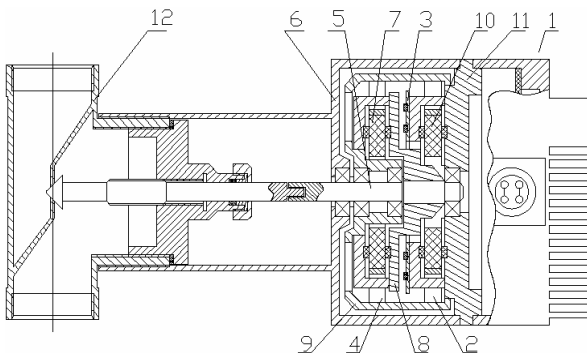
Исполнительный механизм: 1 - защитная крышка блока питания; 2 - толкатели нижнего осциллятора; 3 - токосъемное устройство; 4 - толкатели верхнего осциллятора; 5 - вал; 6 - корпус; 7 - верхний осциллятор; 8 - подвижное основание; 9 - ротор; 10 - нижний осциллятор; 11 - основание; 12 - вентиль
